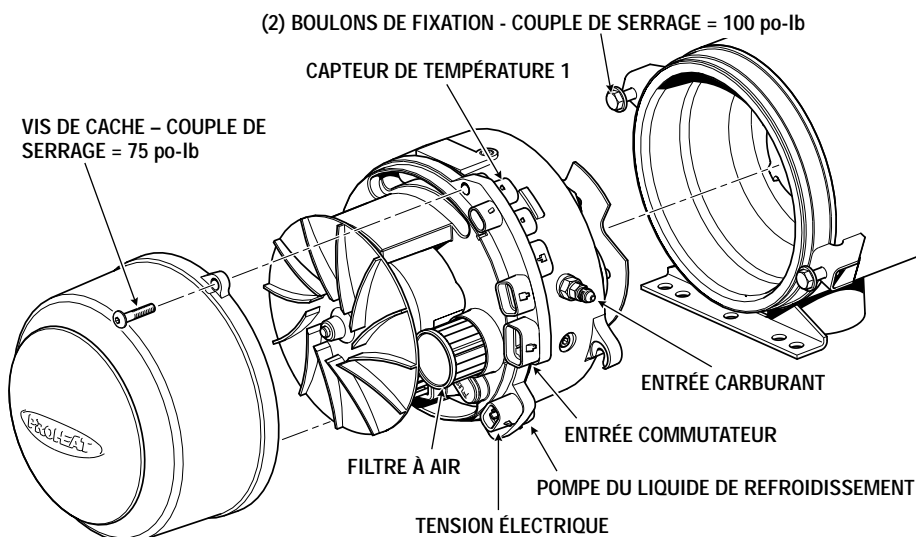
Retrait de la tête de combustion et du cache de la soufflante
